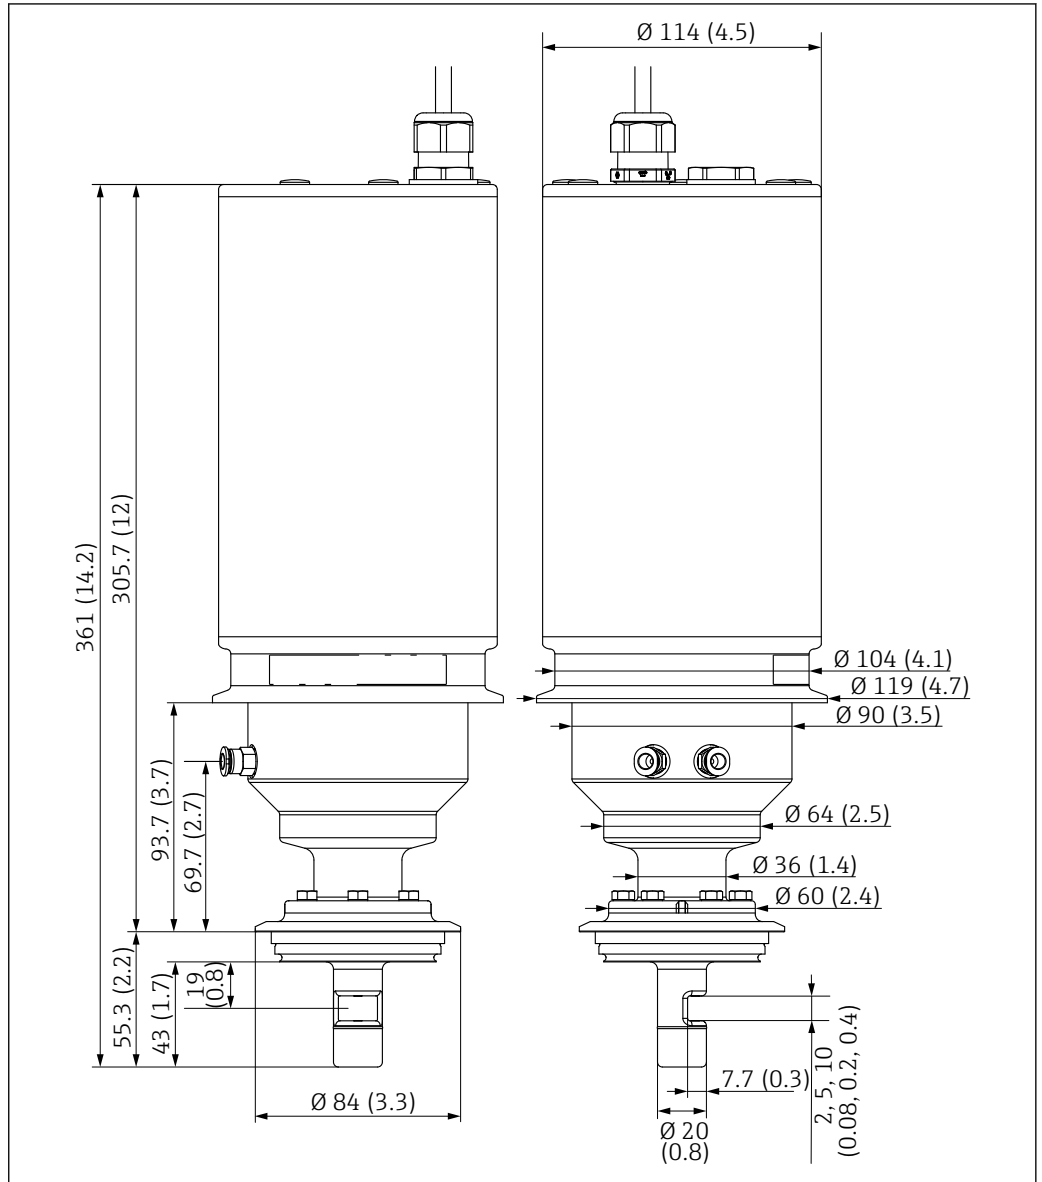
CKI50 的外形尺寸示意图; 单位: mm (in)
